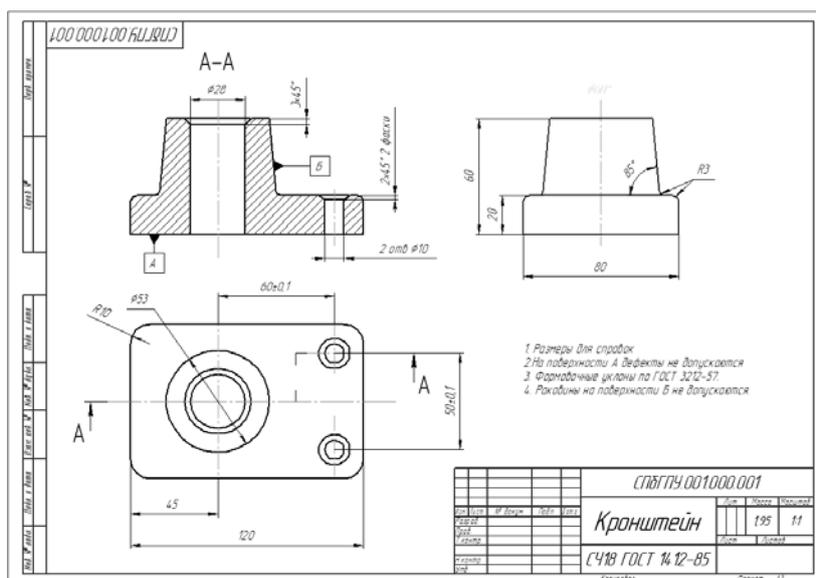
Ассоциативный чертёж детали Кронштейн.
